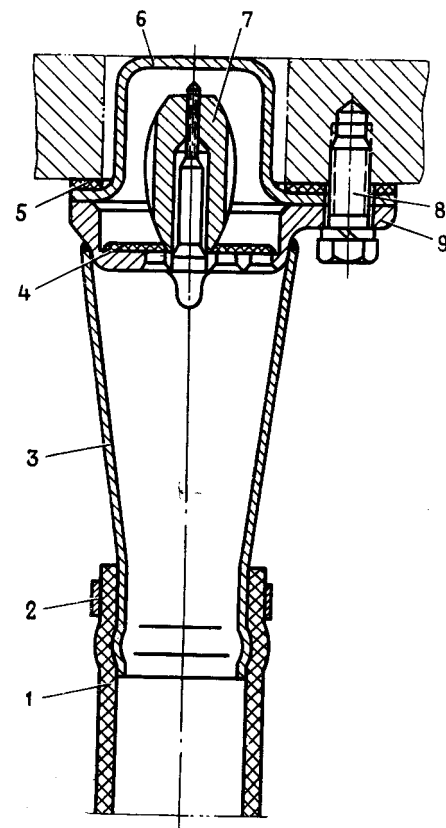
Наконечник с обратным клапаном: 1 — соединительный шланг; 2 — хомут; 3 — наконечник; 4 — обратный клапан; 5 — резиновая прокладка; 6 — крышка; 7 — обтекатель; 8 — болт; 9 — седло
